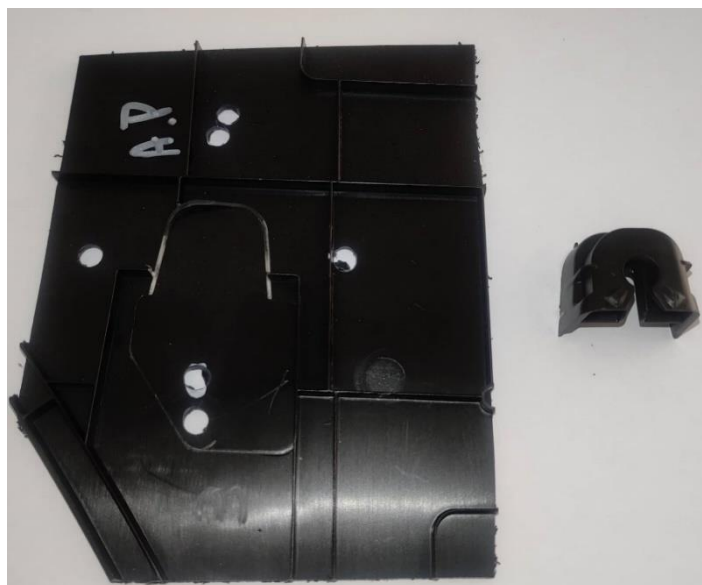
Fixação da posição 3 após ensaio de arrancamento.
